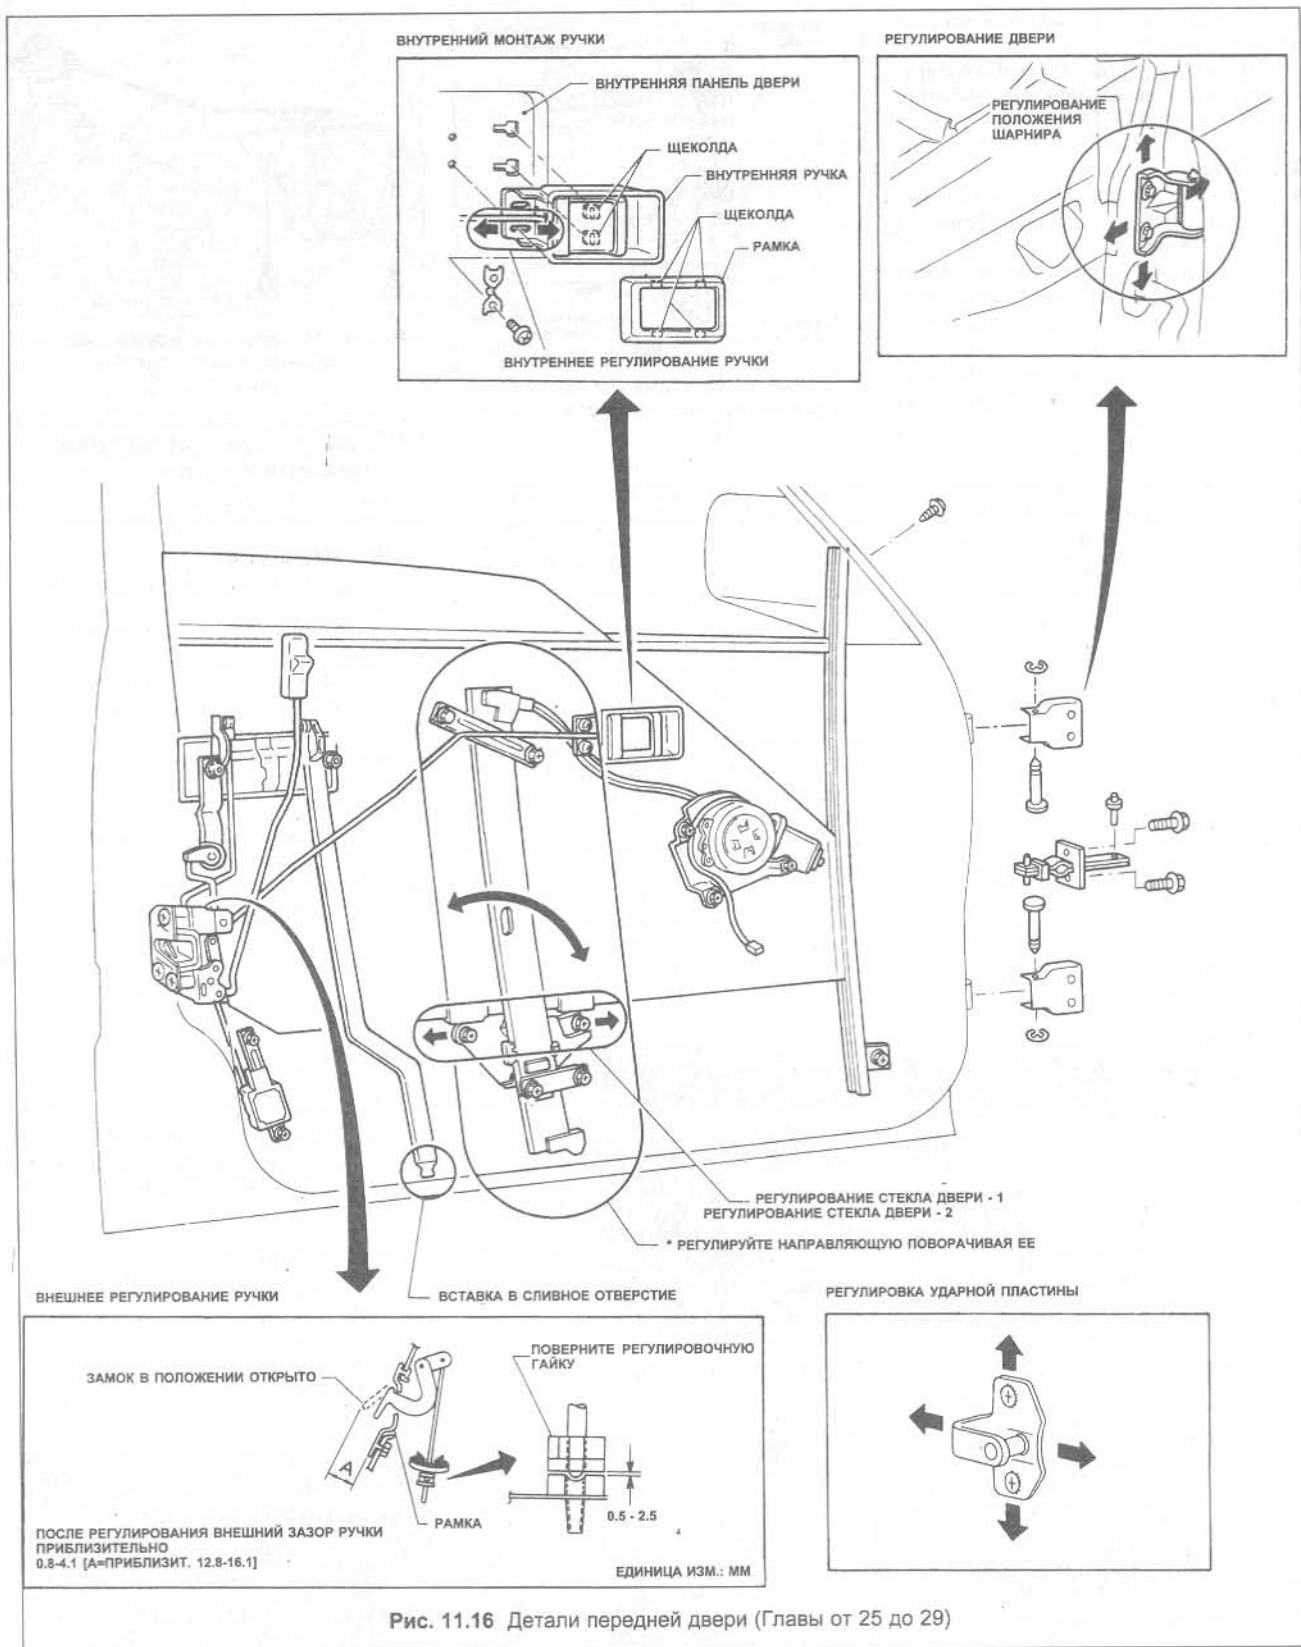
Детали передней двери (Главы от 25 до 29)
